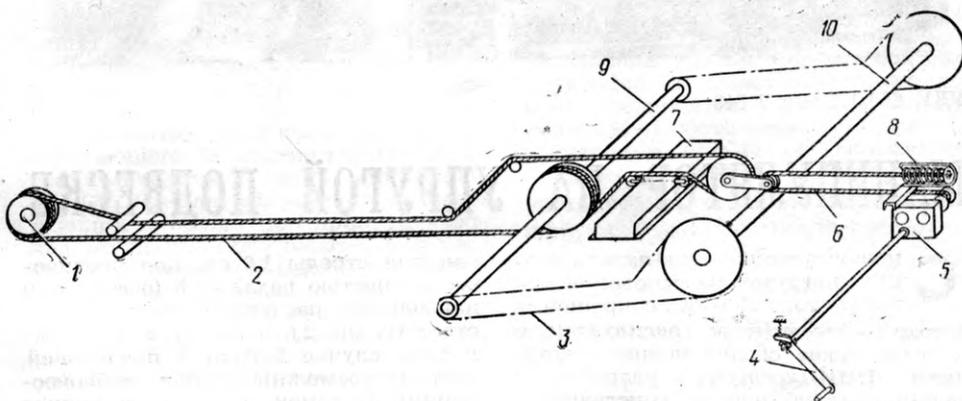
Усовершенствованный привод разгружающего устройства щеповоза
